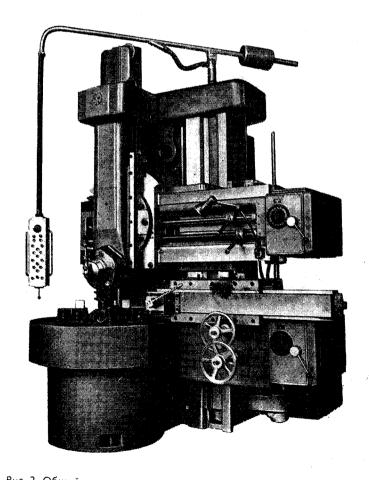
Общий вид токарно-карусельного станка модели 1541
